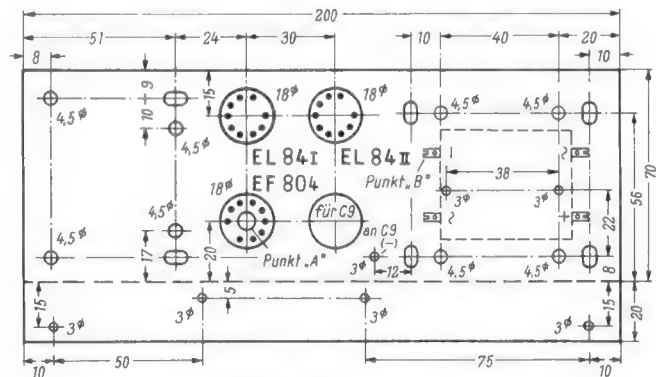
Maße der senkrechten Montagewand mit Bohrungen für die Röhrenfassungen und die Befestigungslöcher
